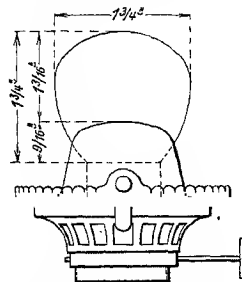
Miller sun hinge-Brenner Nr. 2.
